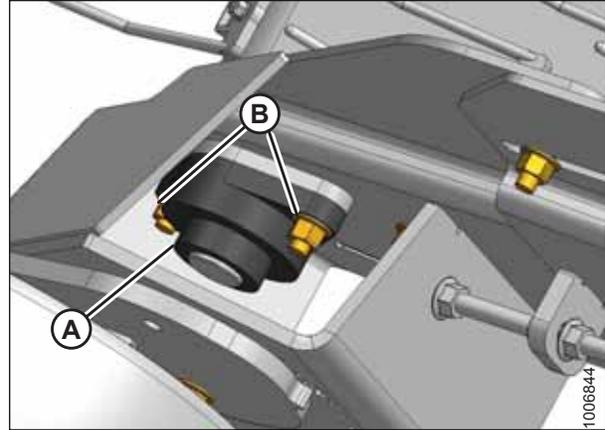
Rodillo tensor de la plataforma frontal izquierda
